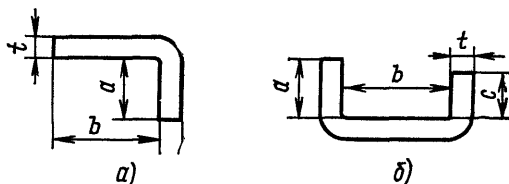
Определение длины заготовок без закруглений (с острыми вершинами внутренних углов)
